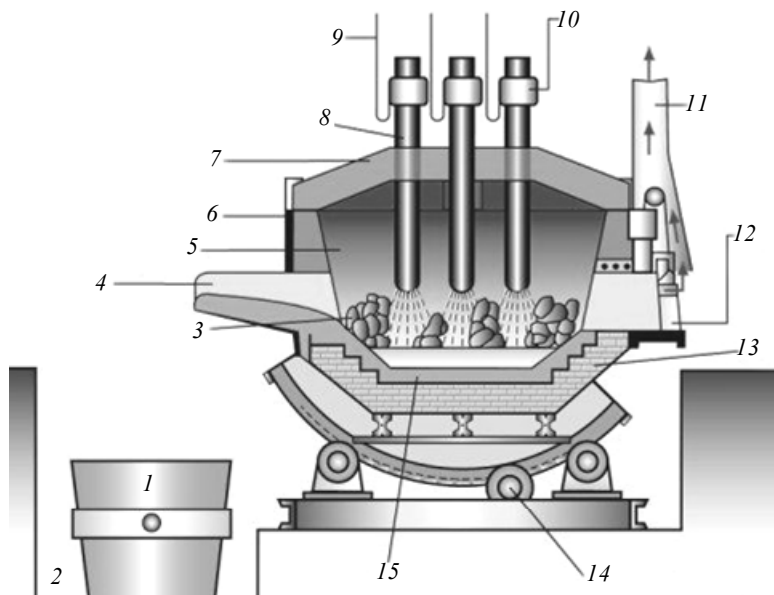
Дугова сталеплавильна піч: 1 – сталеливарний ківш; 2 – приямок; 3 – шихта; 4 – жолоб для зливу сталі; 5 – робочий простір печі; 6 – сталевий кожух; 7 – знімний звід печі; 8 – розхідні вуглецеві (графітні) електроди; 9 – електрокабель; 10 – електродотримач; 11 – газовідвід; 12 – робоче вікно для зливу шлаку, додання феросплавів, взяття проб на аналіз; 13 – футеровка з цегли; 14 – привод для нахилу поду печі; 15 – наварна футеровка подины
